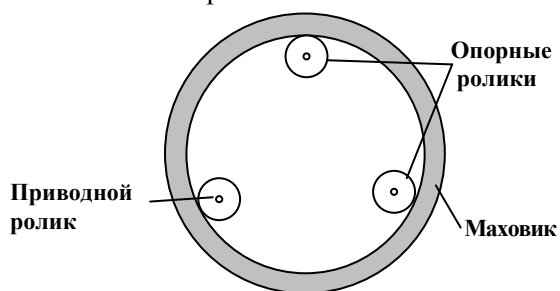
Кинематическая схема кольцевого двигателя-маховика
